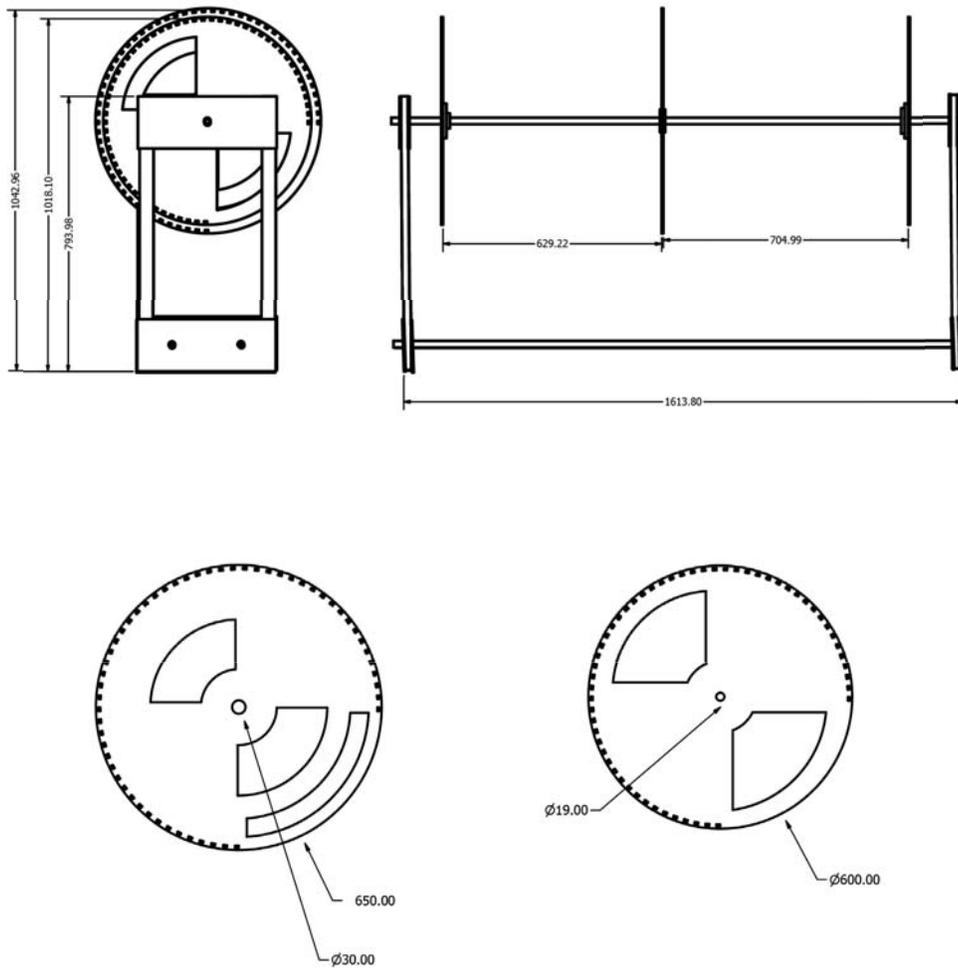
Planos de la estructura último ensayo. Realizado por Camila Campos.
